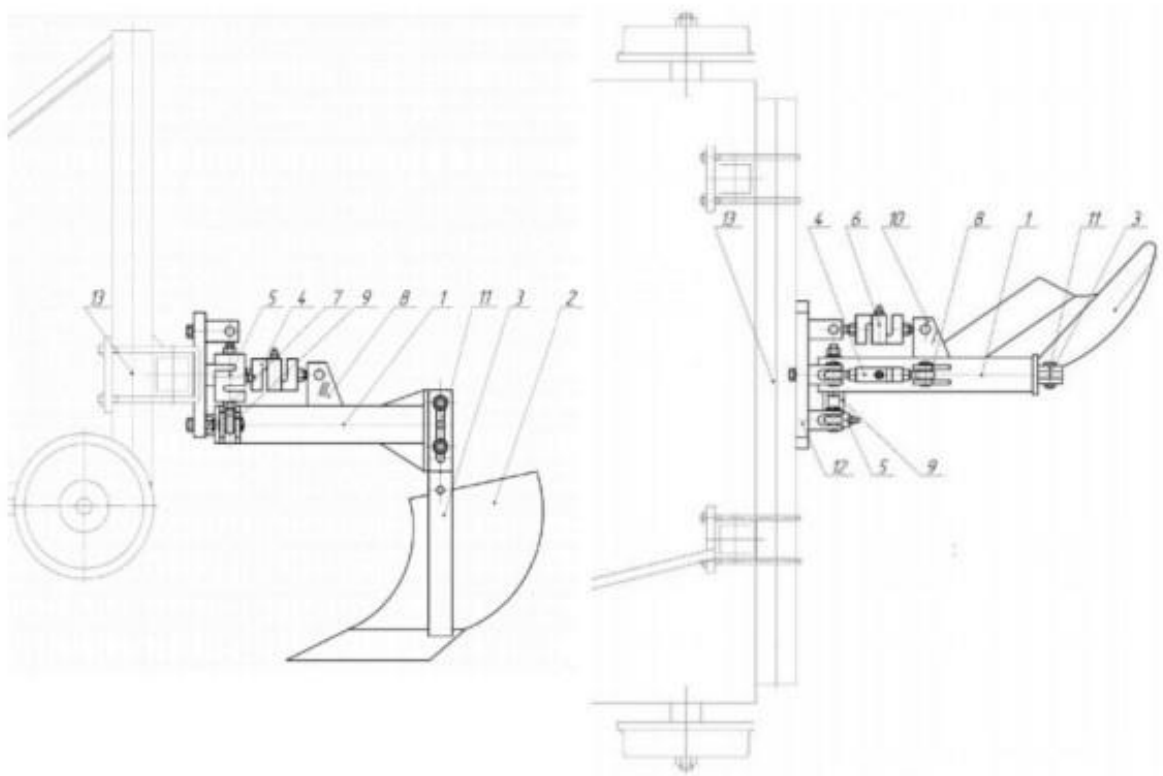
Експериментальний візок з модулем, для просторового динамометрування корпусу лемішно-полицевого плуга: а) вид збоку; б) вид зверху.
